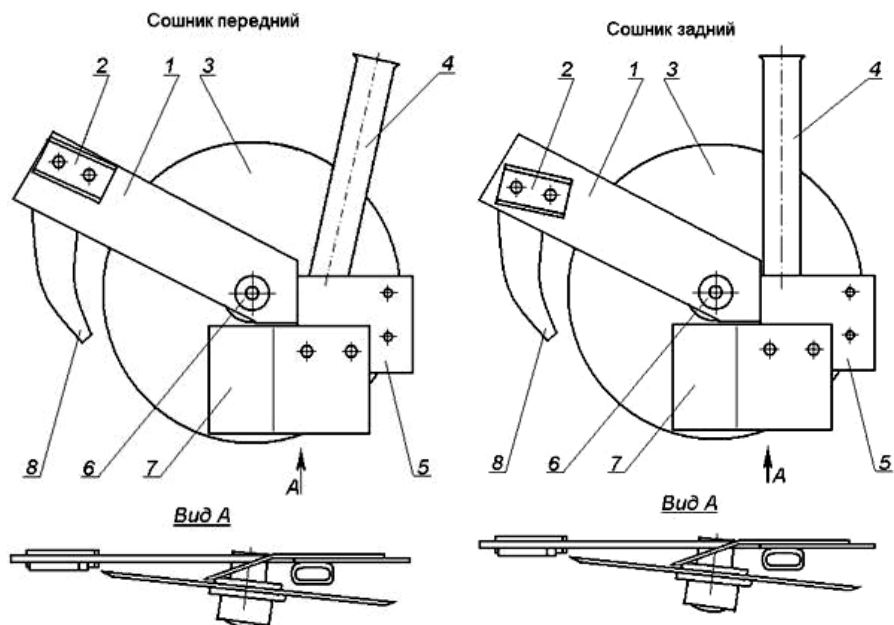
Схема однодисково-анкерного сошника полосного посева: а) передний, б) задний, 1 – корпус сошника, 2 – узел крепления к поводку, 3 – диск сошника со ступицей и осью в сборе, 4 – труба семятукпровода, 5 – монтажный кронштейн, 6 – державка оси, 7 – чистик-анкер-ложеобразователь, 8 – предохранитель
